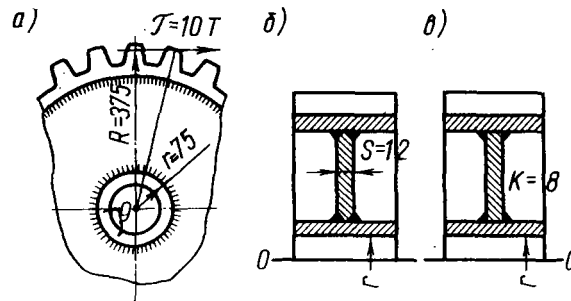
К расчету сварных соединений шестерен со сплошным центром:
